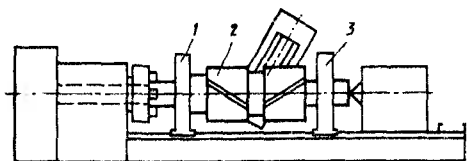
Схема установки заготовки крупного вала-шестерни на горизонтальном зубофрезерном станке:
